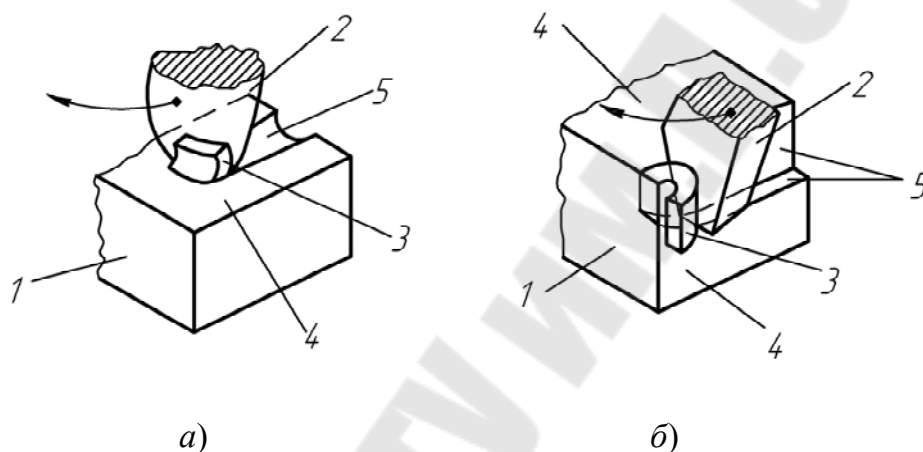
Схема процесса резания при абразивной (а) и лезвийной (б) обработках: 1 – заготовка 3; 2 – режущий инструмент И; 3 – стружка С; 4 – обрабатываемая поверхность; 5 – обработанная поверхность
